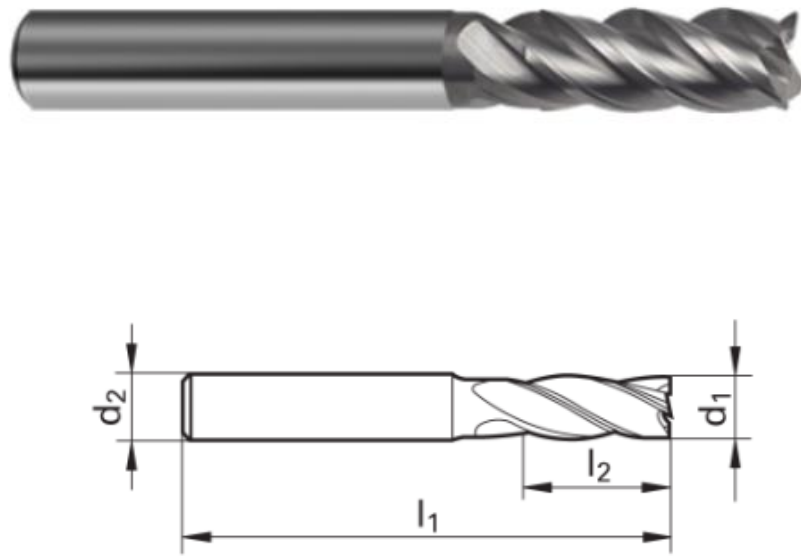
фреза RF 100 A (Guhring) [30]
